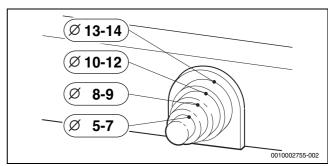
Zugentlastung an Kabeldurchmesser anpassen
